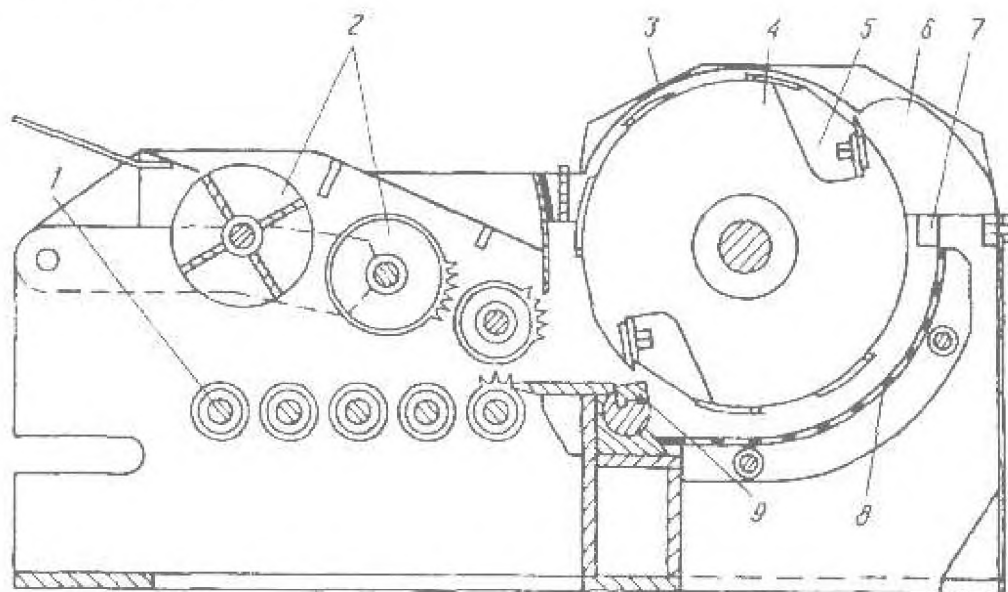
Барабанна рубальна машина ДО-51: 1 та 2 - відповідно нижні привідні вальці та верхні притискні (привідні) вальці; 3 - кожух ножового (різцевого) барабана; 4 - різцевий барабан; 5 - підножова пазуха; 6 - захисний елемент кожуха; 7 - додатковий контрніж; 8 - сепарувальна решітка; 9 - нижній (основний) контрніж
